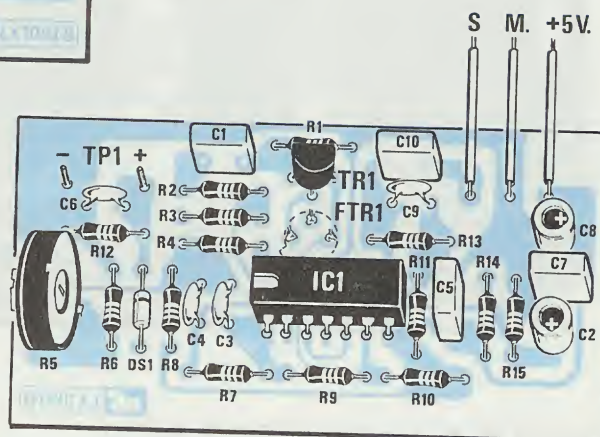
Schema pratico di montaggio del fotorivelatore LX.1091/B. Il fototransistor BPW.77 andrà montato dal lato opposto di questo stampato (vedi disegno sopra) rivolgendo la tacca di riferimento a destra.
